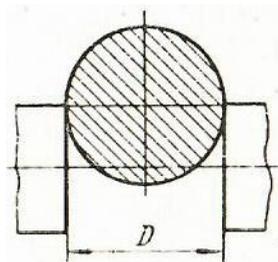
Возможное положение детали между плоскими измерительными поверхностями пяток
